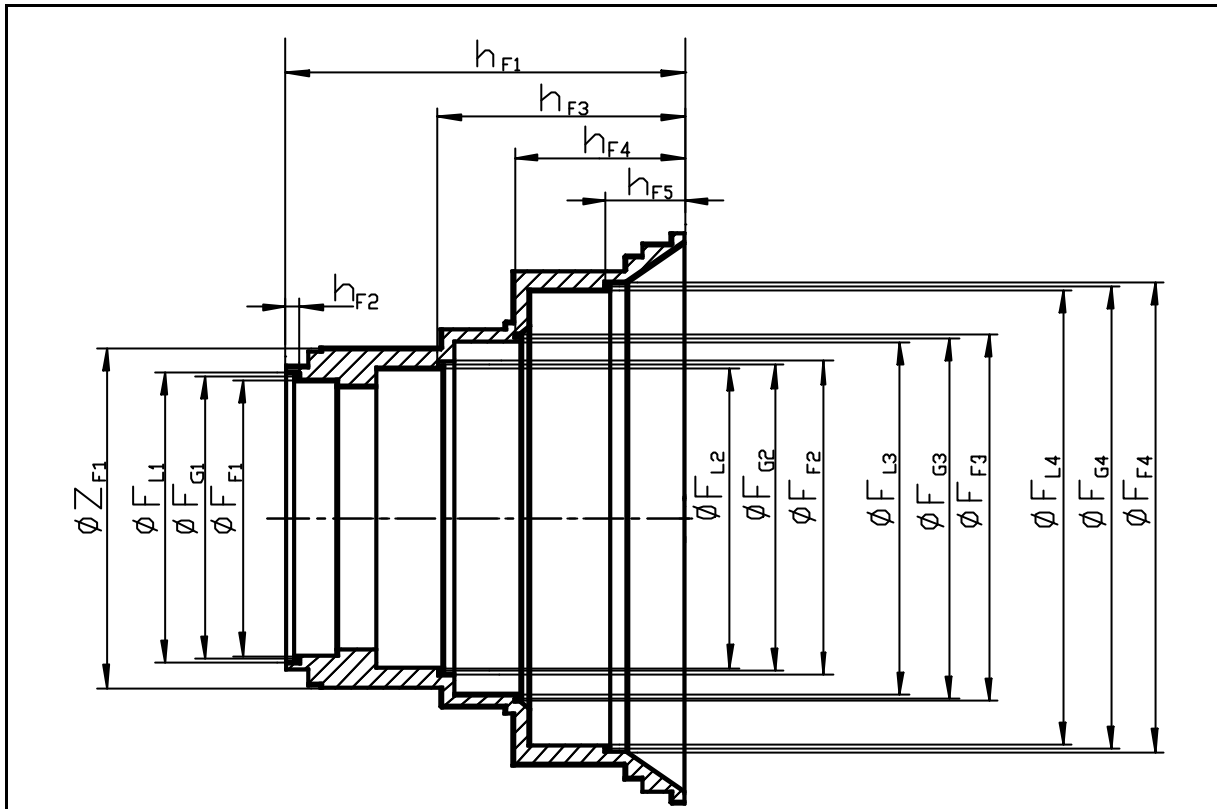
Fassungsbeispiel mit verfahrenstechnisch wichtigen Maßen
